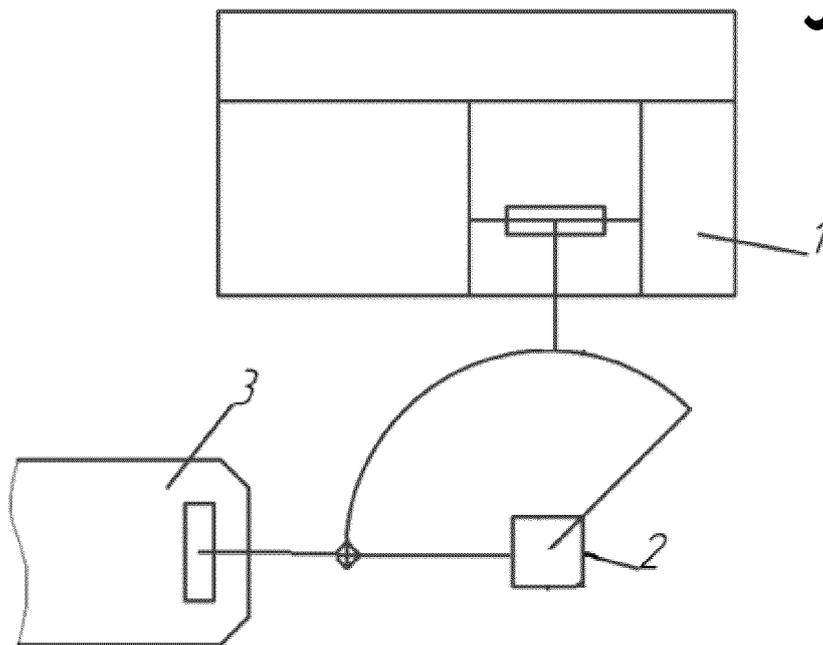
Кільцева компоновка робочого місця з промисловим роботом
